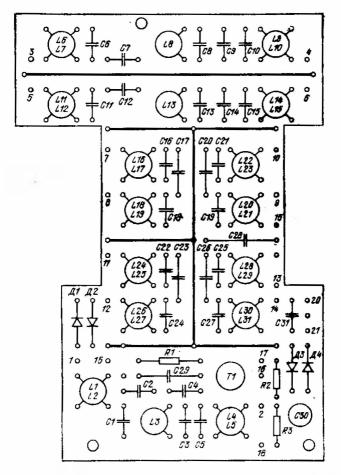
Мочтажная схема платы усилителя ВЧ (вид сверху)
